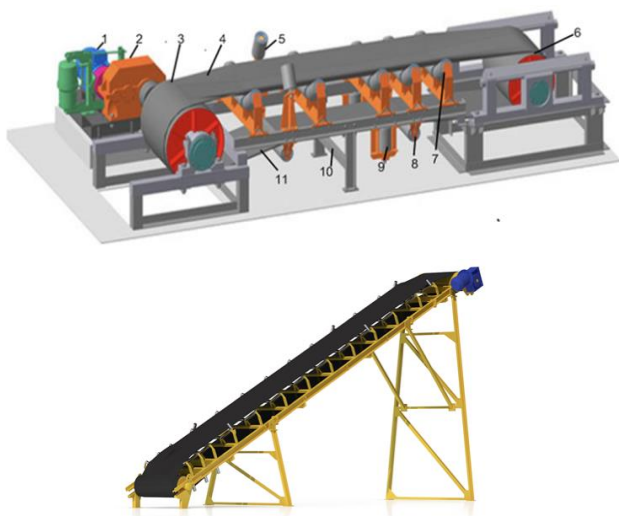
Стрічковий транспортер: 1 – приводний електродвигун; 2 – редуктор привода; 3 – приводний барабан; 4 – робоча гілка стрічки конвеєра; 5, 9 – ролики проти сходу, відповідно робочої та холостої стрічки; 6 – натяжний барабан; 7, 8 – підтримуючі ролики, відповідно робочої та холостої стрічки; 10 – рама; 11 – неробоча стрічка конвеєра
